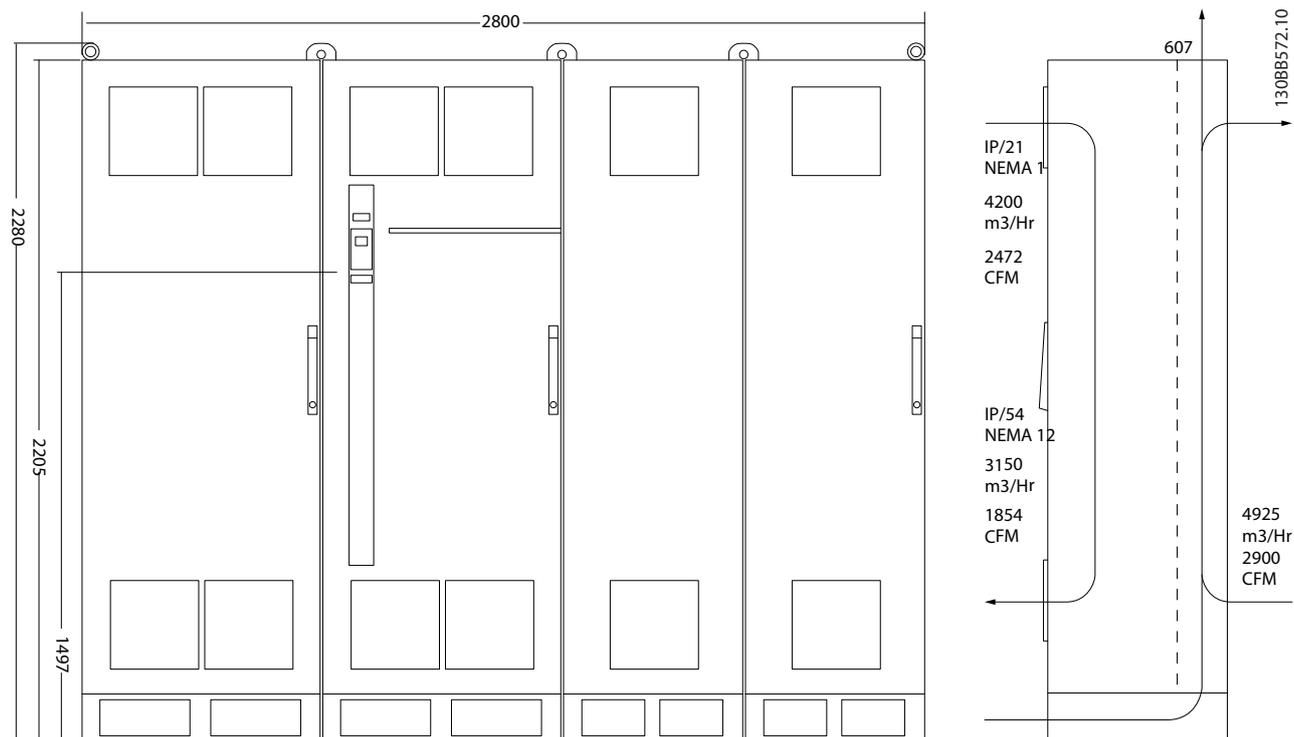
Dimensiones mecánicas (mm), F13
